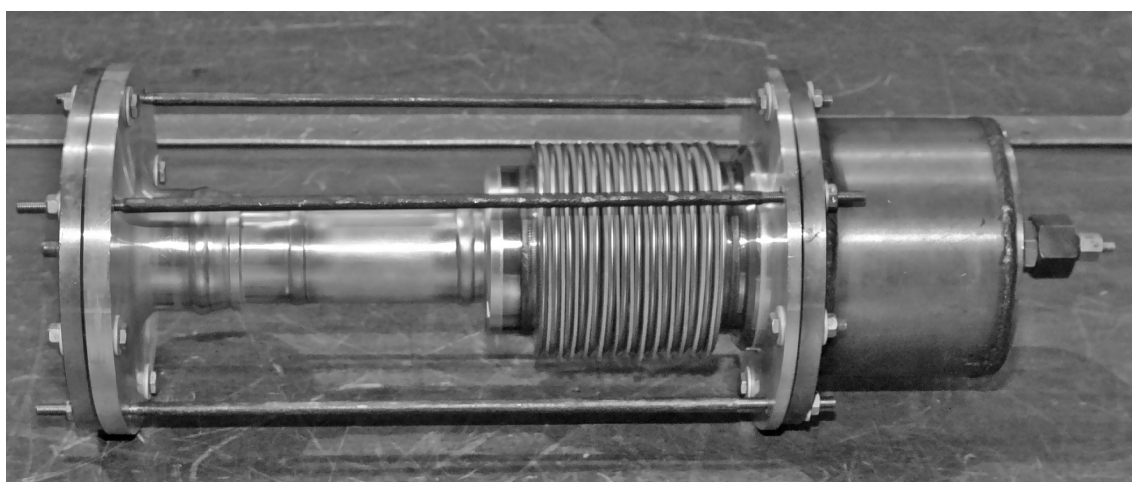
Опытная конструкция стального компенсатора с биметаллическими переходниками
